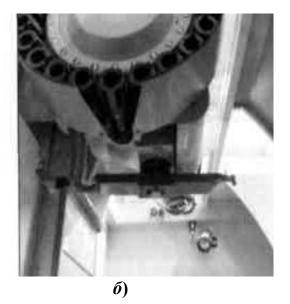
Механизмы смены инструментов вертикальных станков:
